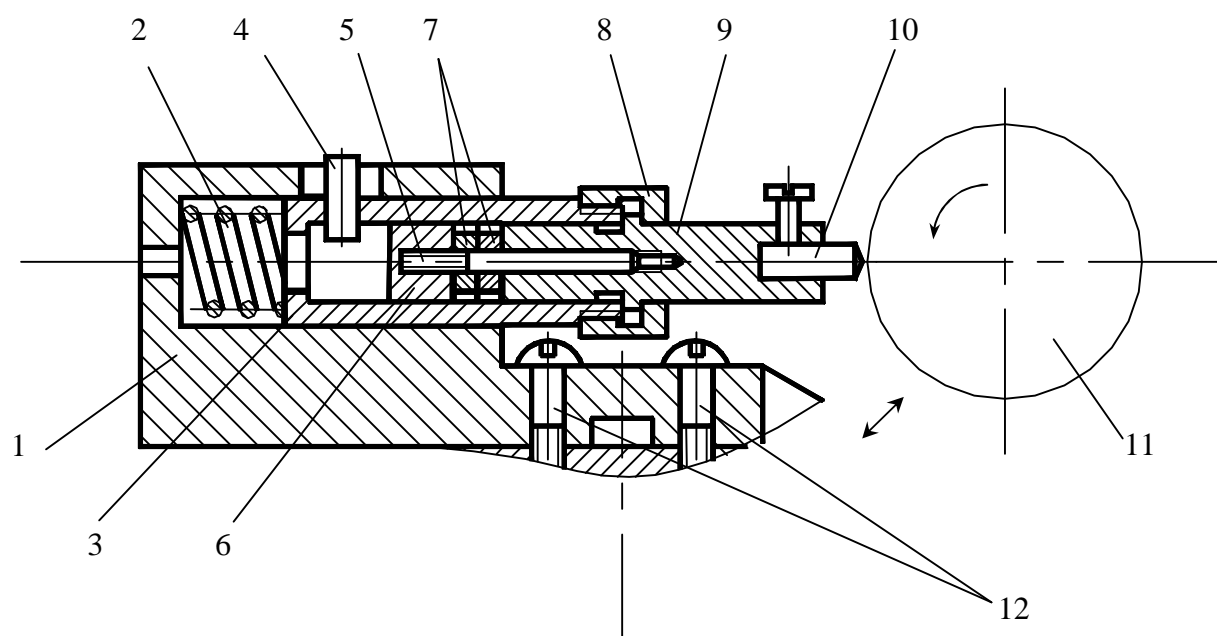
Устройство для алмазного выглаживания заготовок с наложением ультразвуковых колебаний: 1 – корпус; 2 – пружина; 3 – стакан; 4 – штифт; 5 – шпилька; 6 – гайка; 7 – пьезокерамические кольца; 8 – гайка; 9 – волновод; 10 – алмазный выглаживатель; 11 – заготовка; 12 – винты
